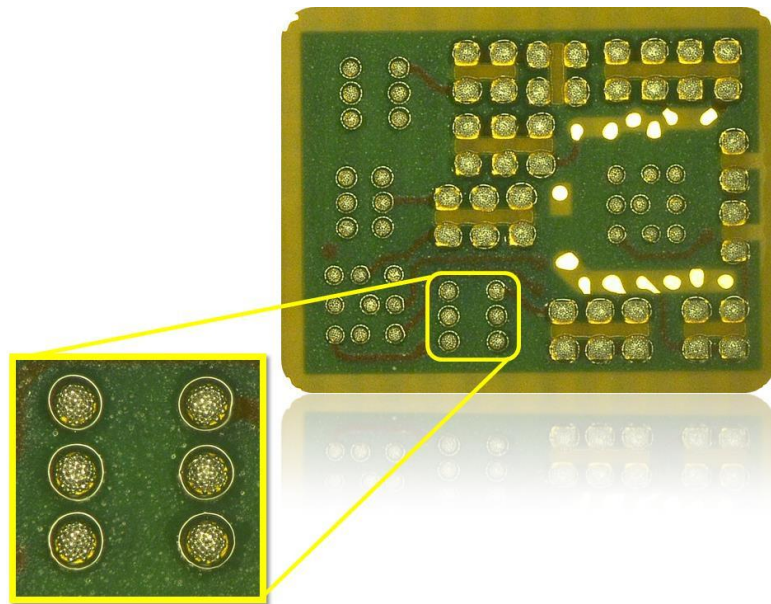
Impresión de soldadura de pasta usando soldadura tipo V
